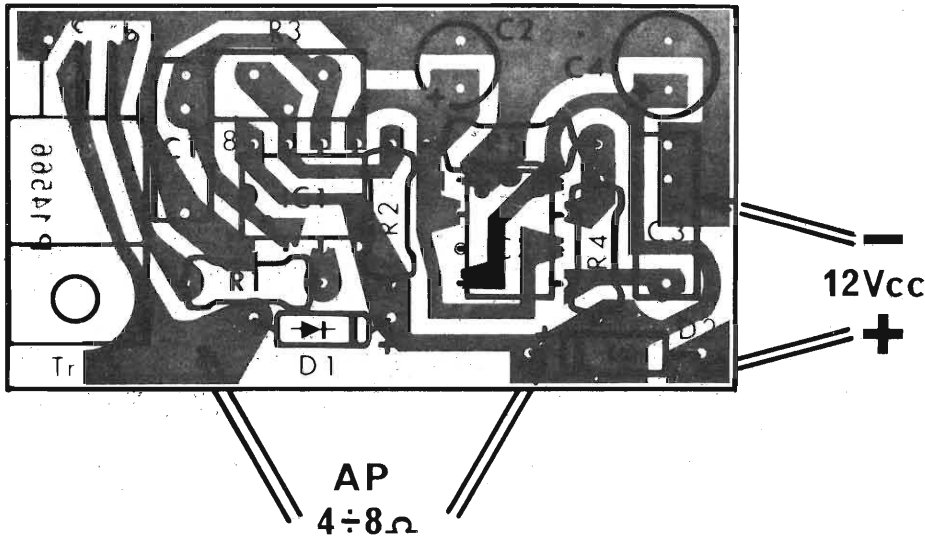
Basetta a circuito stampato vista in trasparenza e disposizione dei componenti.
